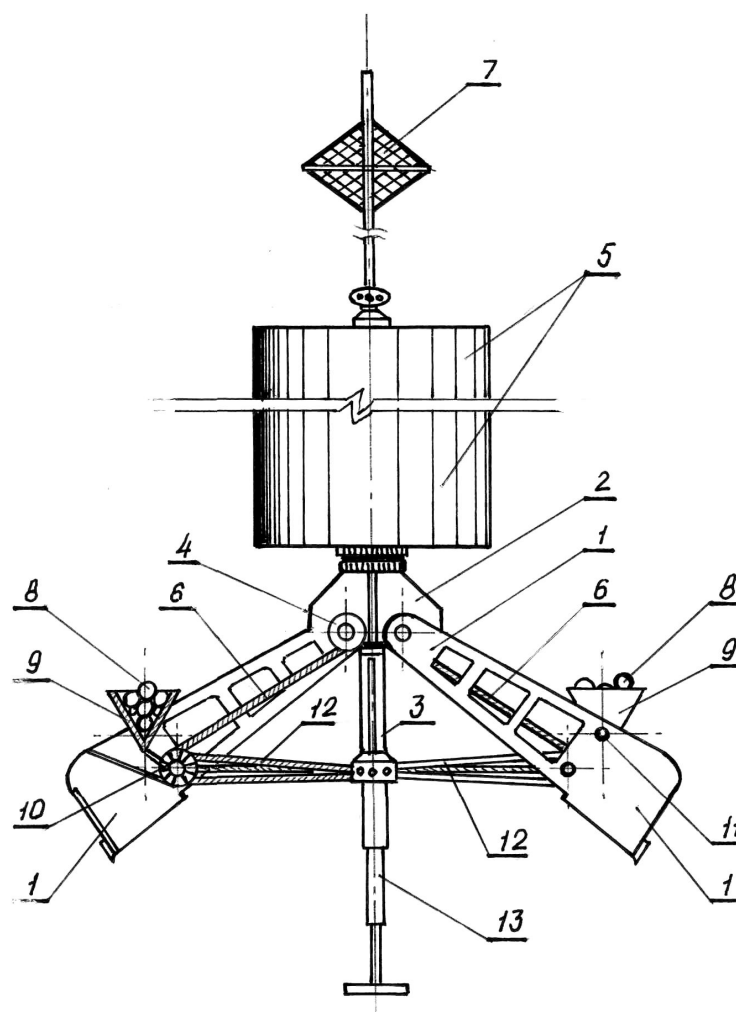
Схема самовсплывающего дночерпателя (автономного пробоотборника) модели АП-6000 [48]: 1 – створки грейферного ковша; 2 – опорная рама; 3 – направляющая штанга; 4 – шкив; 5 – поплавковый модуль; 6 – гибкая тяга; 7 – устройство для поиска АП на поверхности океана (отражатель); 8 – балластные грузы; 9 – контейнеры; 10 – упоры; 11 – оси поворота контейнеров; 12 – синхронизирующие штанги; 13 – шток-лидер
